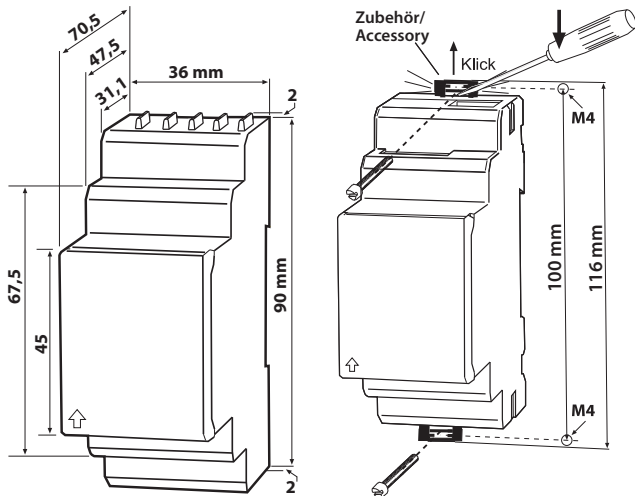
Maßbild, Skizze für Schraubbefestigung
